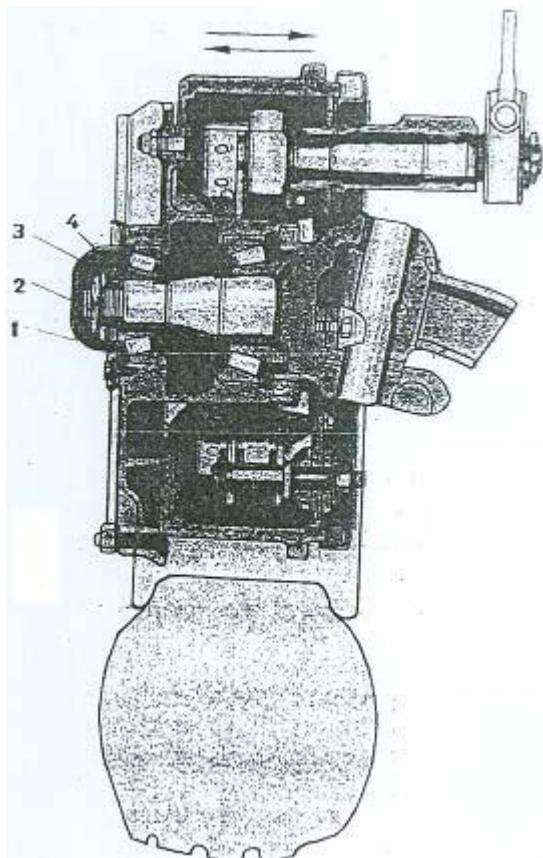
Проверка зазора между шкворнем и подшипником скольжения.
